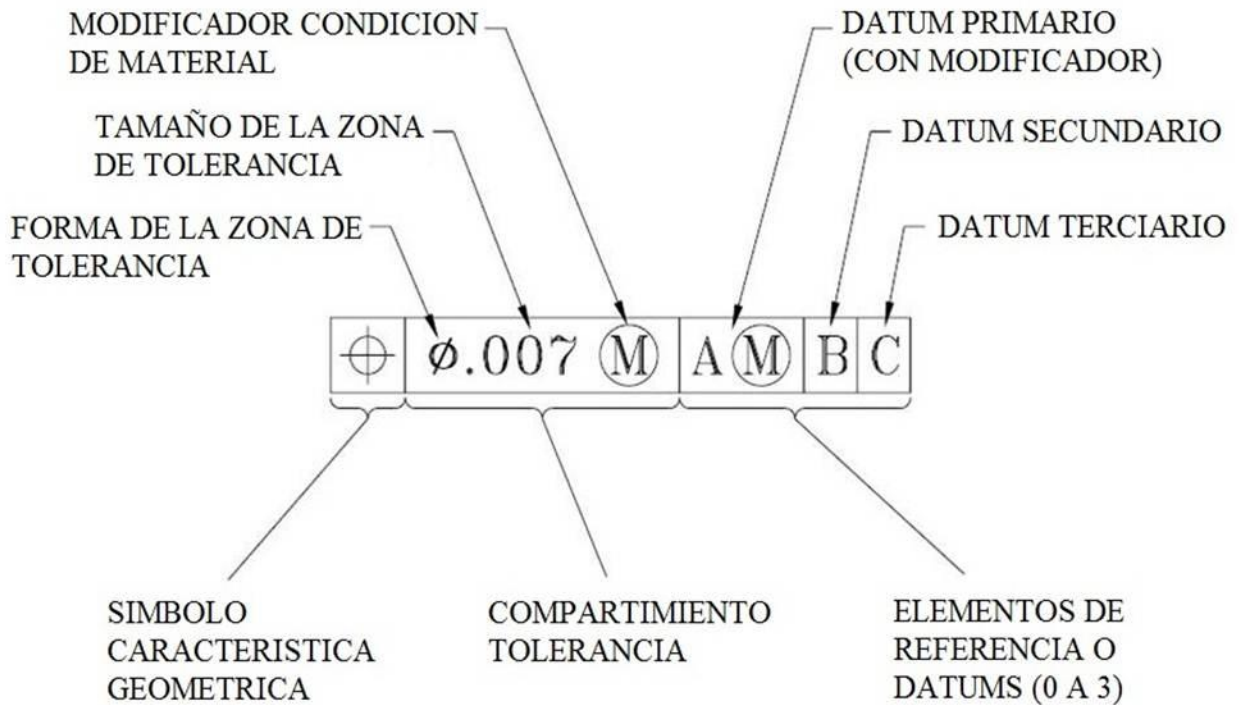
Marco de control Básico para el dimensionamiento Geométrico y tolerancias.
